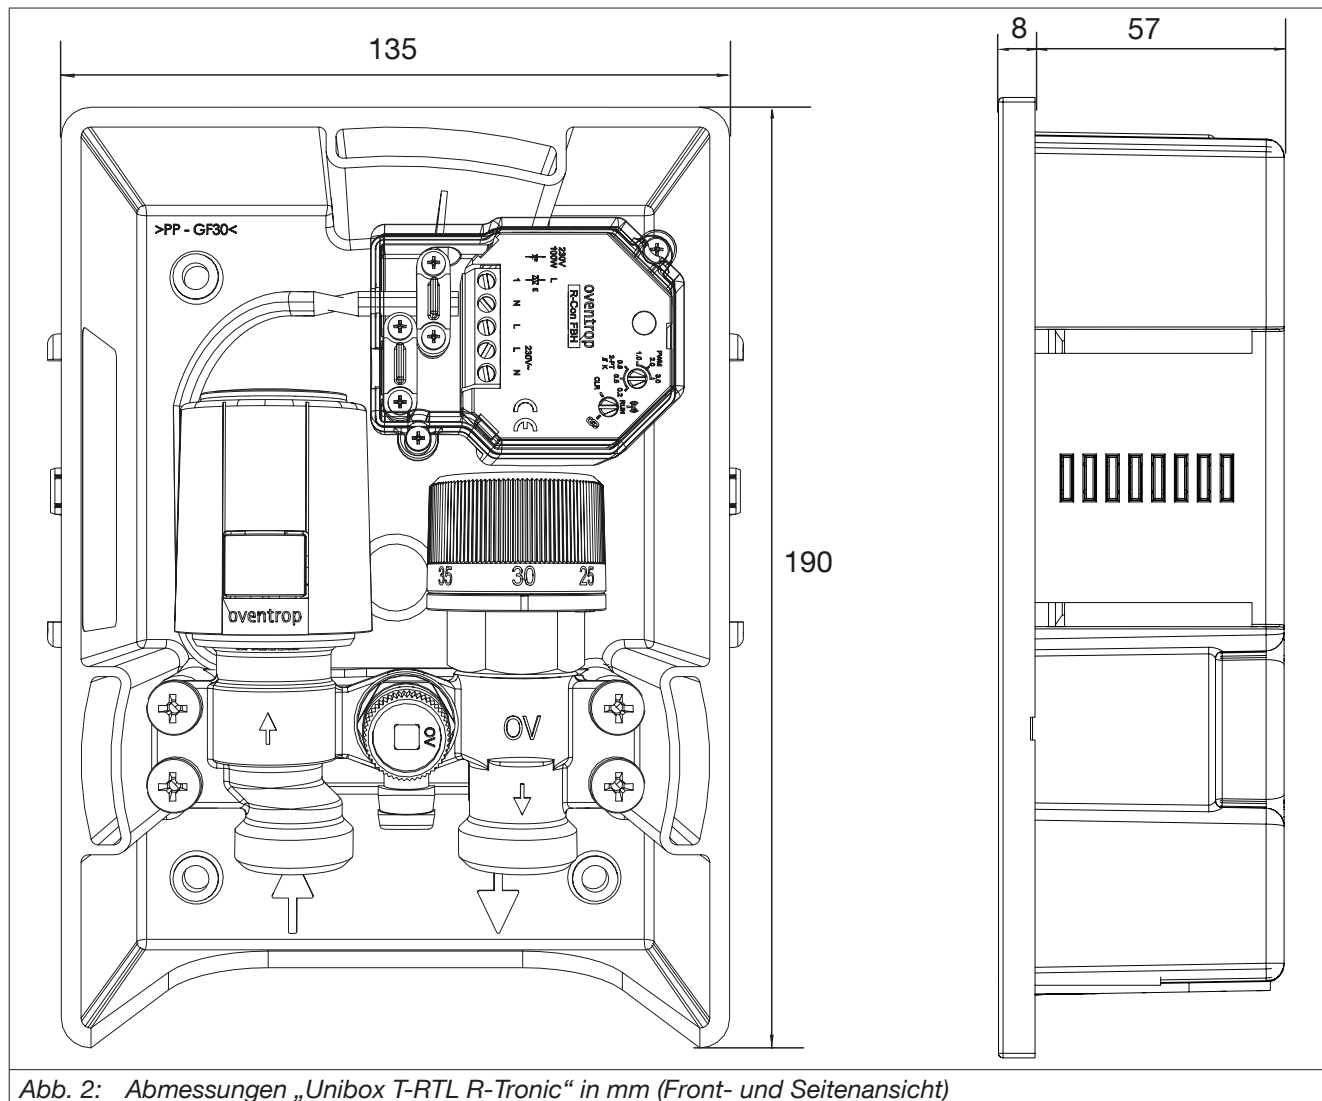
Abmessungen „Unibox T-RTL R-Tronic“ in mm (Front- und Seitenansicht)
